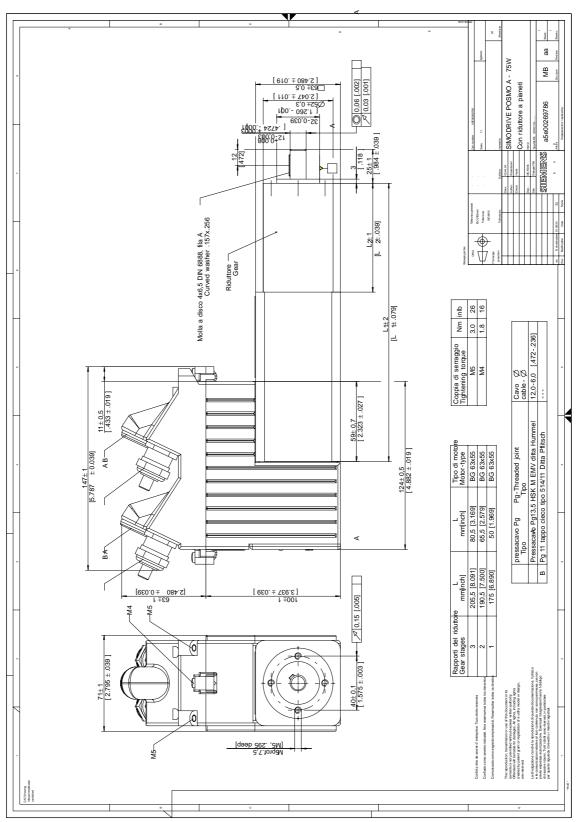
Dimensioni: SIMODRIVE POSMO A da 75 W con riduttore a pianeti
